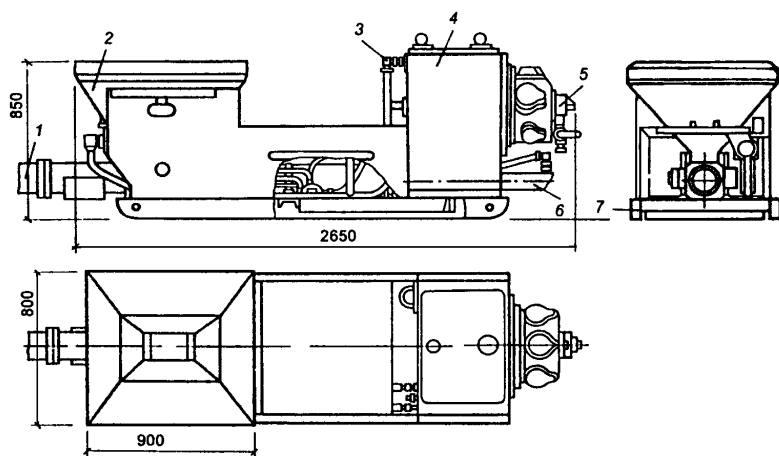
Бетононасос СБ-161: 1 – бетоновод; 2 – бункер; 3 – гидросистема; 4 – гидропривод; 5 – кран; 6 – рабочий цилиндр; 7 – рама
